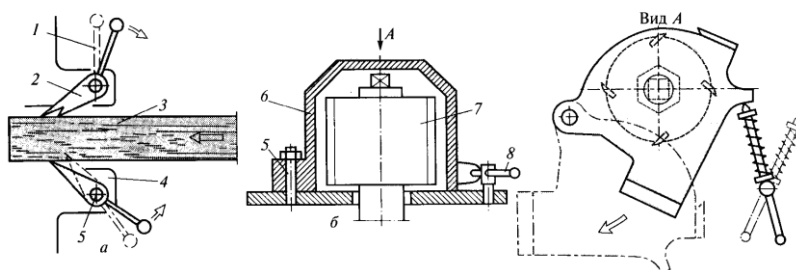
Запобіжні пристрої: *а* – когтевий захист; *б* – огороження; 1 – рукоятка; 2 – пазури; 3 – заготовка; 4 – верстат; 5 – вісь; 6 – ковпак; 7 – фреза; 8 – рукоятка-фіксатор
